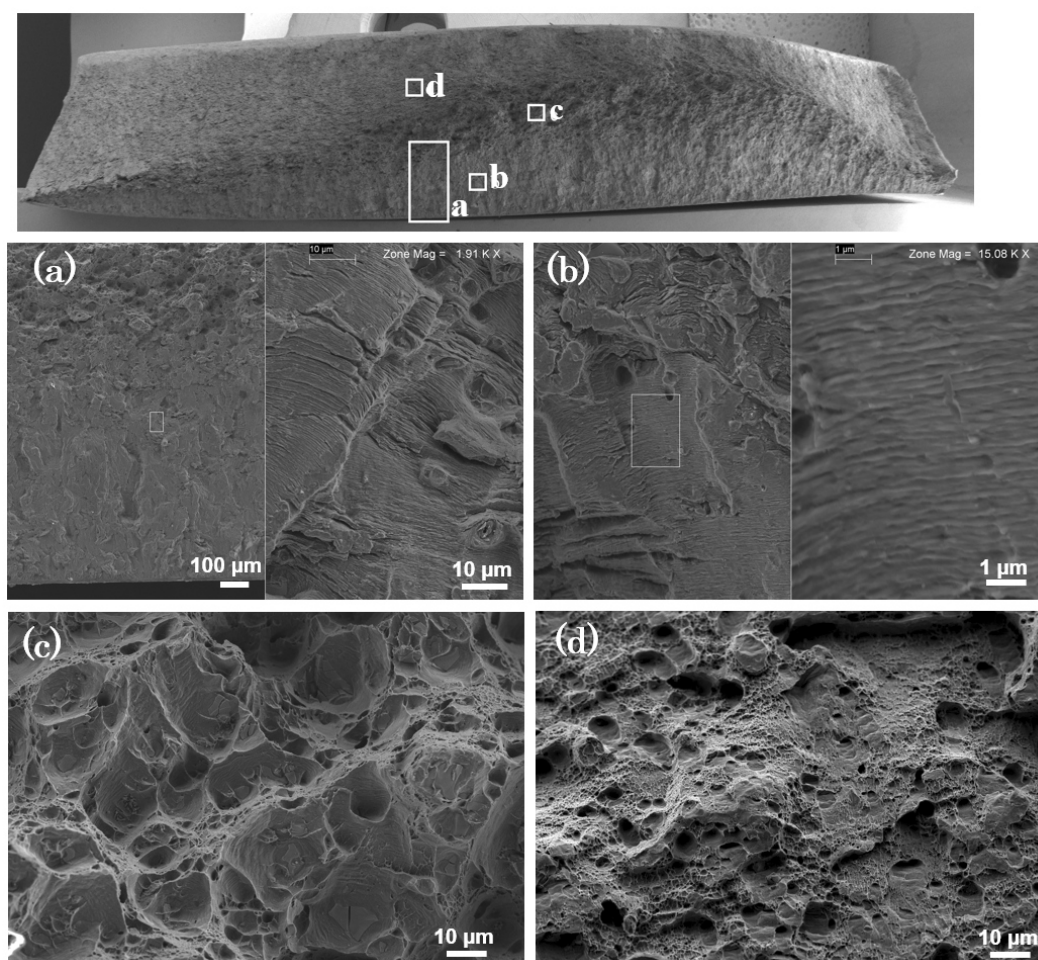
Superfícies de fratura da soldadura DLPP-65-116: (a) e (b) fraturas por fadiga; (c) e (d) fraturas dúcteis.
